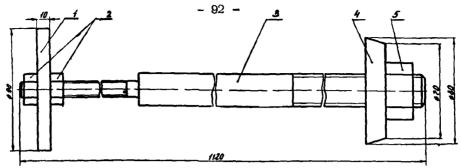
Приспособление для разборки и сборки механизмов камеры:
